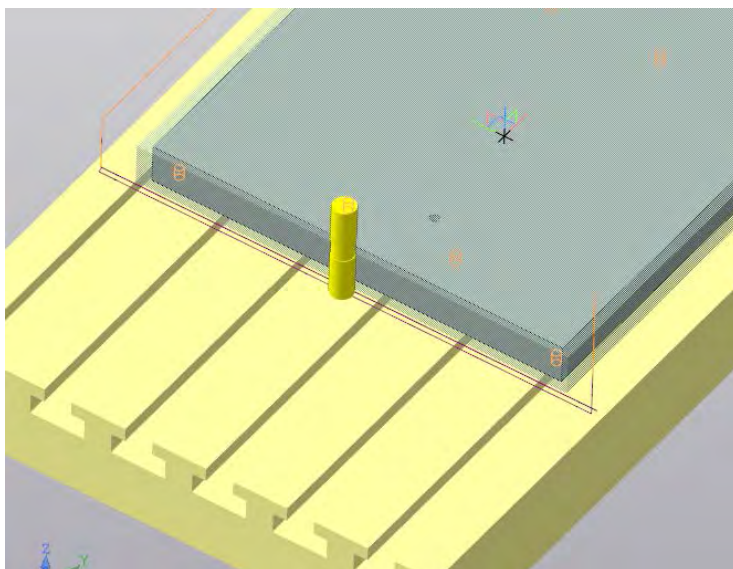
Визуализация процесса фрезерования габаритов заготовки
